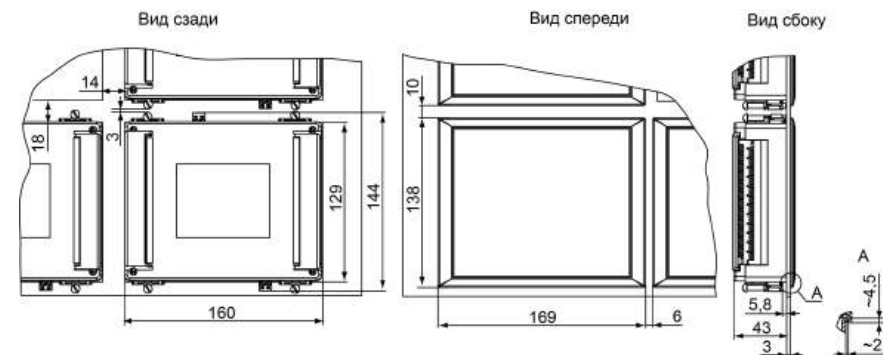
Прибор в корпусе Щ7, установленный в щит толщиной 3 мм
